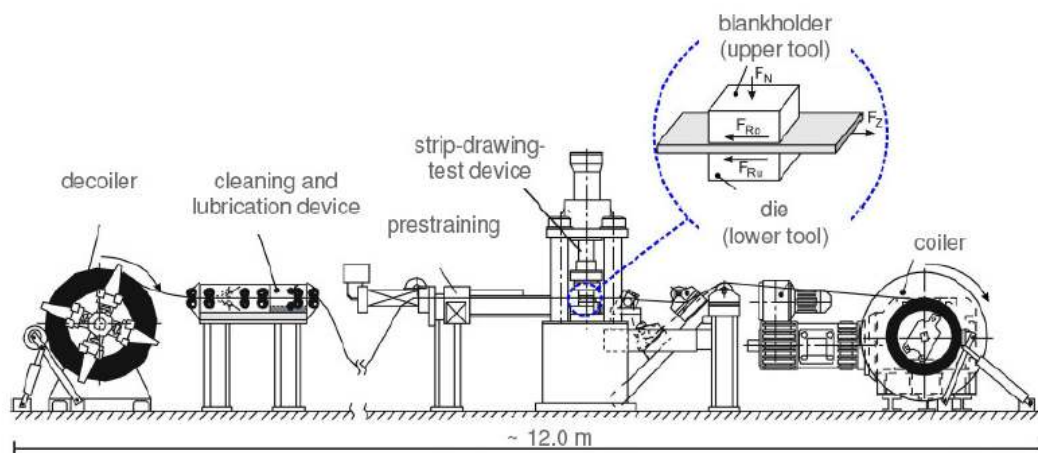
Representação do dispositivo montado para a realização do “*strip drawing test*”.
